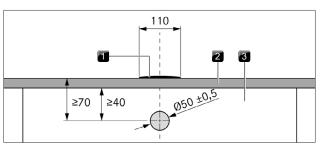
Padrão de perfuração do painel do exaustor de placa
